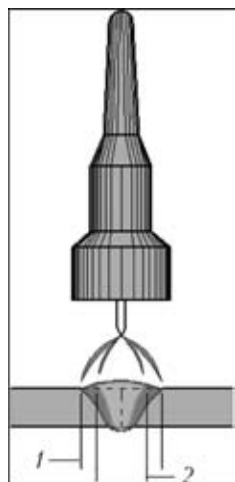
Схема геометрии сечения металла шва при сварке ТИГ с непрерывной (1) и импульсной (2) дугой
